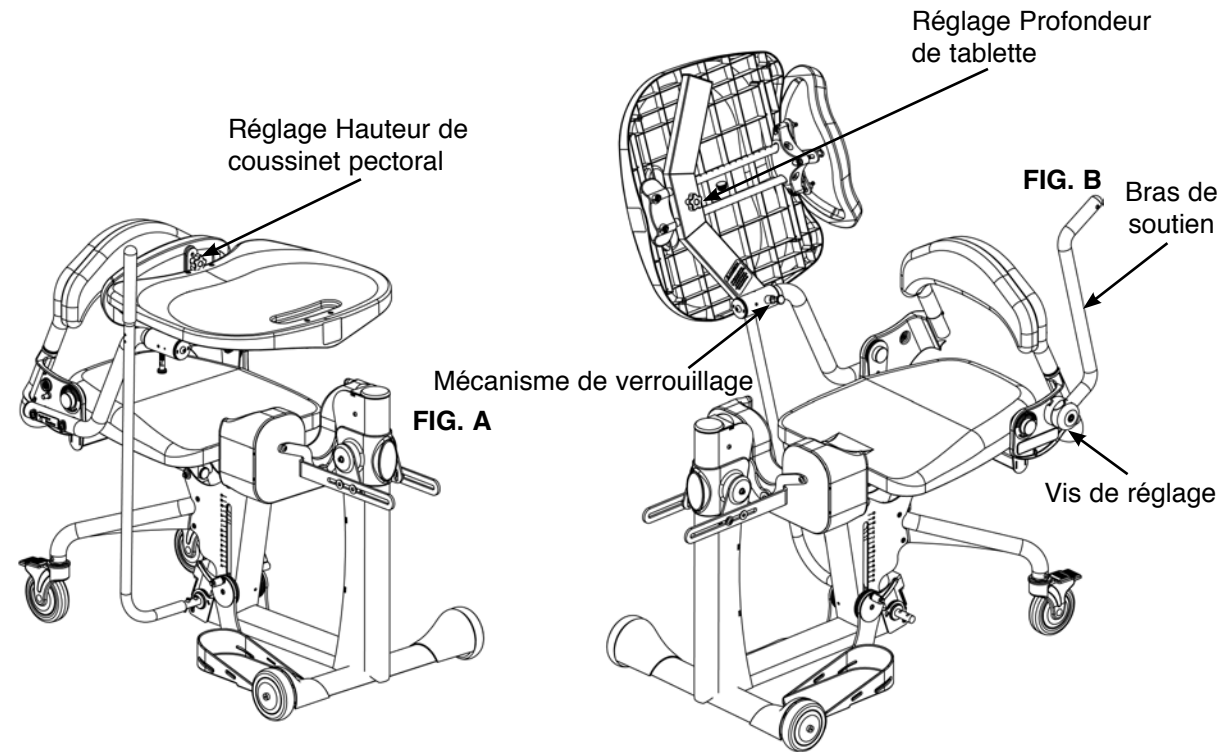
FIG. A- Pour régler la hauteur du coussinet pectoral, desserrez la poignée et placez-le à la position souhaitée. Serrez à fond.
